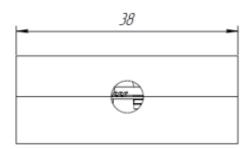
Габаритные размеры ДТЦ-135
